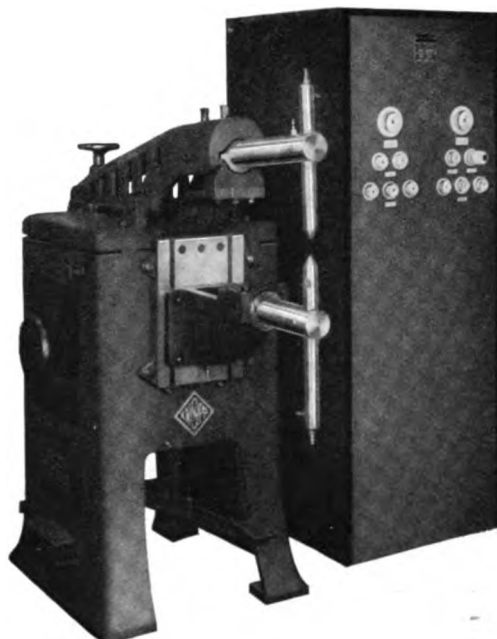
Punktschweißmaschine für Flugzeugbau mit Stromrichterschrank.
